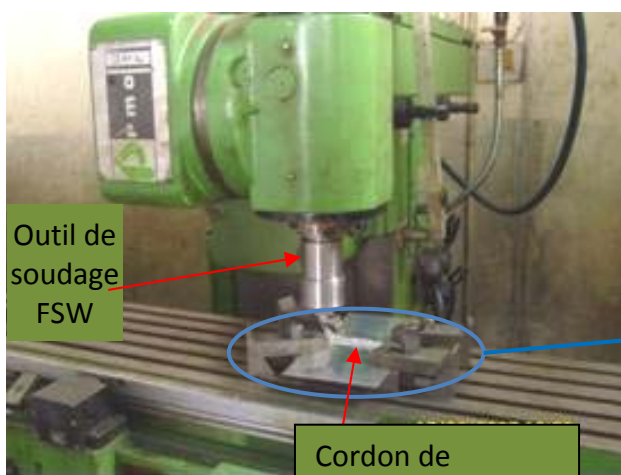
Machine de fraisage exploitée dans le procédé FSW.
